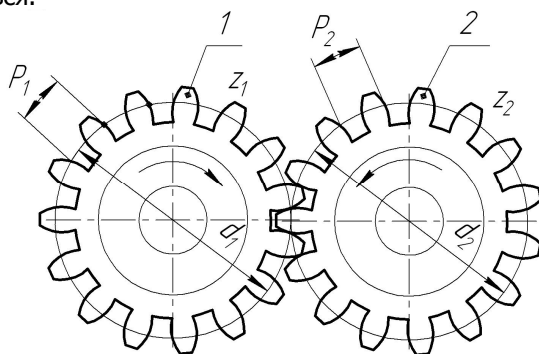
Зубчатая цилиндрическая передача с внешним зацеплением
